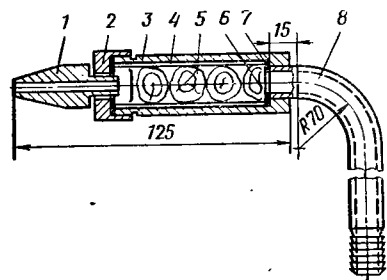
Пылесазорная трубка с фильтровальным патроном из гильзы охотничьего патрона:
